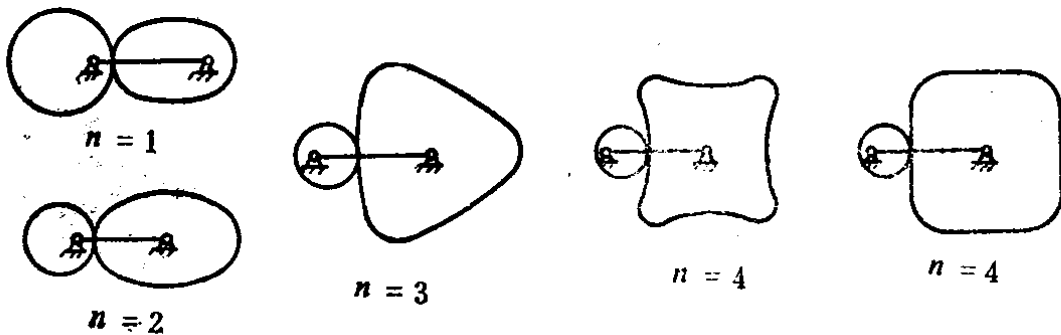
偏心圆齿轮与各种变形椭圆齿轮共轭
